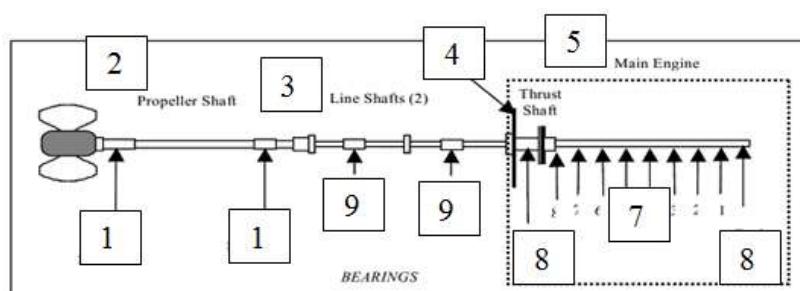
Схема валопровода контейнеровоза типа CV-2600: 1 – кормовой и носовой подшипники дейдвуда; 2 – гребной вал; 3 – валопровод; 4 – маховик; 5 – упорный вал; 6 – главный дизель; 7 – рамовые подшипники; 8 – кормовой и носовой подшипники главного дизеля; 9 – кормовой и носовой подшипники валопровода
